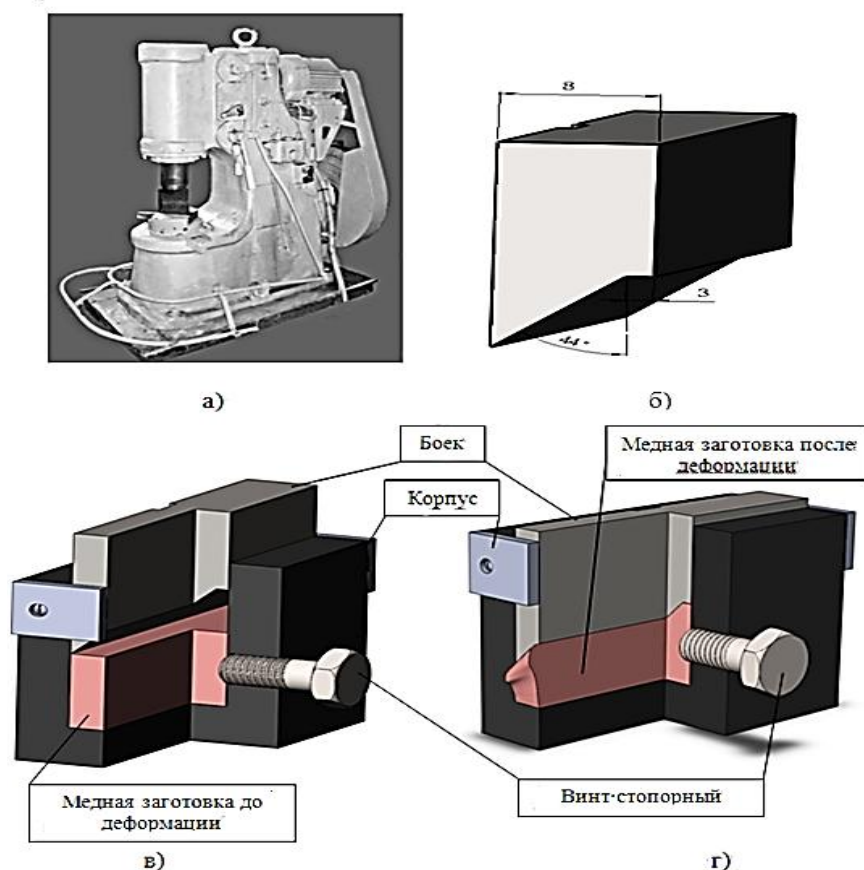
Молот и приспособление для ударно-пластической разделки кромок меди:
